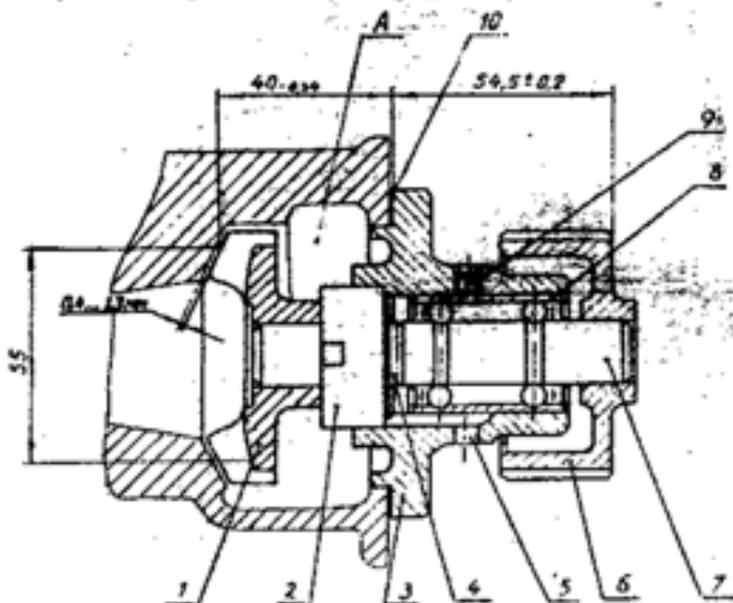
Водяной насос двигателя: 1 - крыльчатка; 2 - манжета; 3 - корпус; 4 - кольцевая канавка на валу; 5 - отверстие для слива жидкости; 6 - шкив водяного насоса; 7 - вал; 8 - шариковый подшипник; 9 - стопорный винт; 10 - прокладка; А - полость насоса
